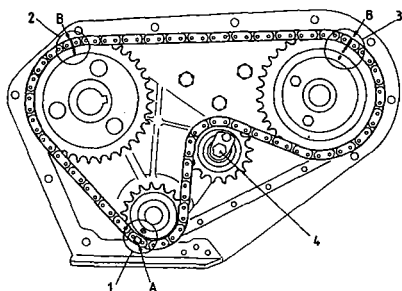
Engranajes con sus marcas de puesta a punto en un motor Diesel de la marca PEUGEOT. La cadena lleva también marcas que han de coincidir. 1, piñón del cigüeñal. 2, engranaje del eje de levas. 3, idem de la bomba de inyección. 4, tensor.
